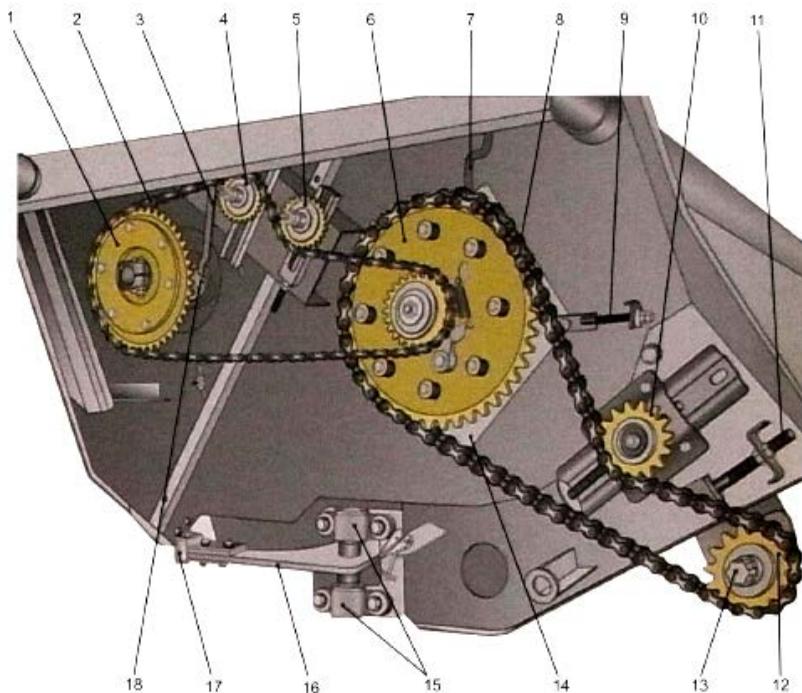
Механизм привода шнека и мотовила: 1 – устройство предохранительное мотовила; 2 – цепь привода мотовила; 3 – тяга регулировки положения мотовила; 4 – обводная звездочка; 5 – натяжная звездочка; 6 – устройство предохранительное шнека жатки; 7 – тяга регулировки шнека по высоте; 8 – цепь привода шнека; 9 – тяга регулировки шнека по горизонтали; 10 – натяжная звездочка цепи привода шнека; 11 – тяга регулировки положения вала контрпривода; 12 – звездочка контрпривода; 13 – вал контрпривода; 14 – плита шнека; 15 – опора колебателя привода ножа; 16 – колебатель привода ножа режущего аппарата; 17 – головка привода ножа; 18 – пластина регулировки положения мотовила и наклона граблей
